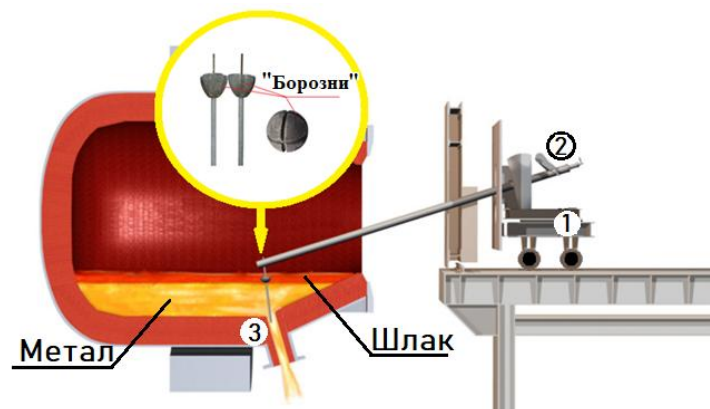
Загальний схематичний вигляд системи вторинного відсікання кінцевого конвертерного шлаку, де 1 - аплікатор (маніпулятор) типу «візок» для подачі стопору в порожнину конвертера, 2 – механічний привід від'єднання стопору від штанги, 3 – сталевипускний канал (лътка).
